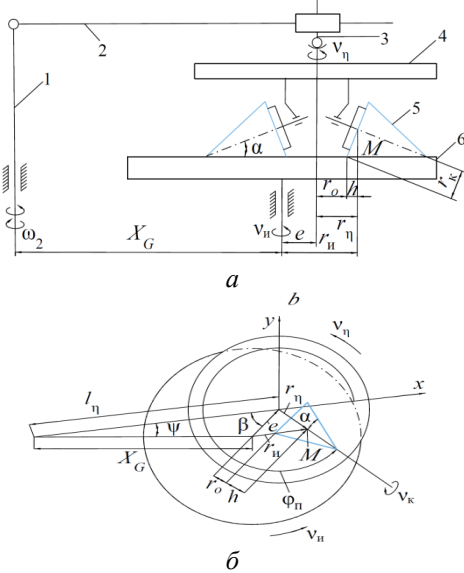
Схема обработки деталей с коническими поверхностями (а) и размерная цепь ее рабочей зоны (б)
